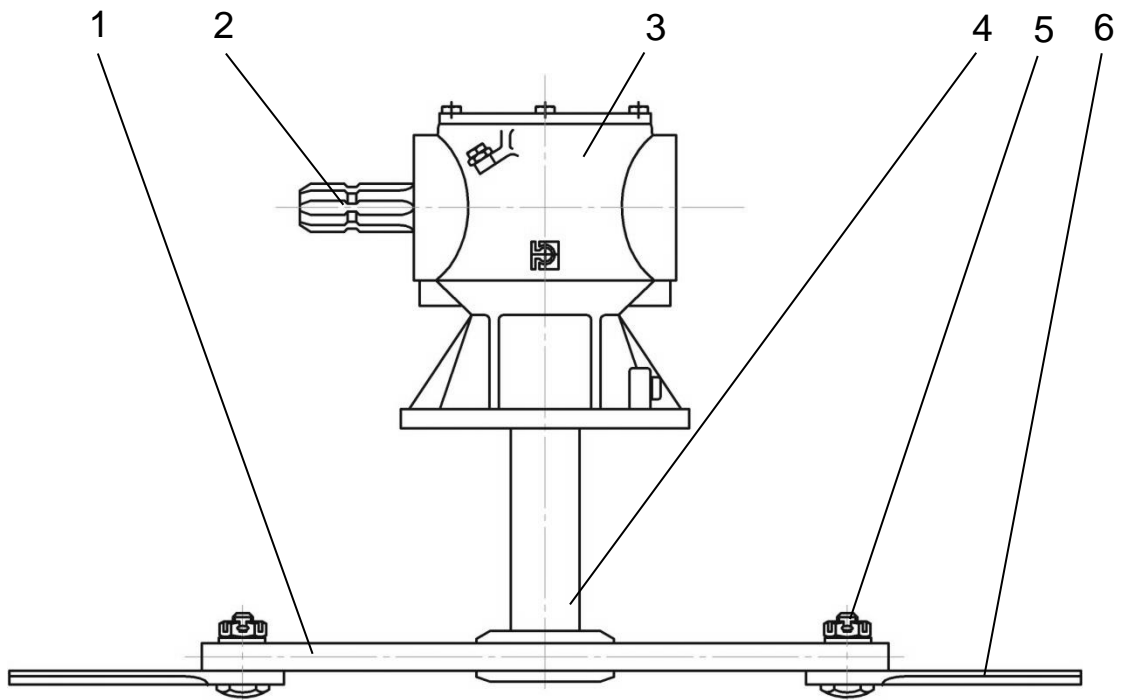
Ротаційний різальний апарат: 1 – тримач; 2 – ведучий вал; 3 – конічний редуктор; 4 – привідний вал; 5 – шарнір; 6 – ніж.
